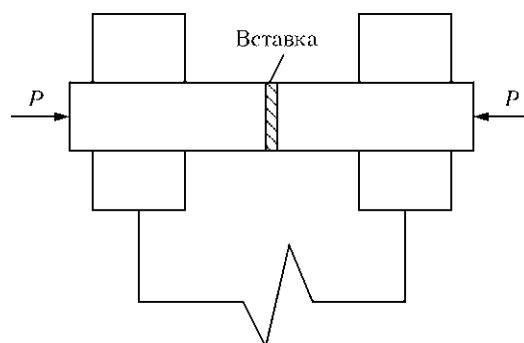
Схема сварки сопротивлением с использованием композитной вставки
